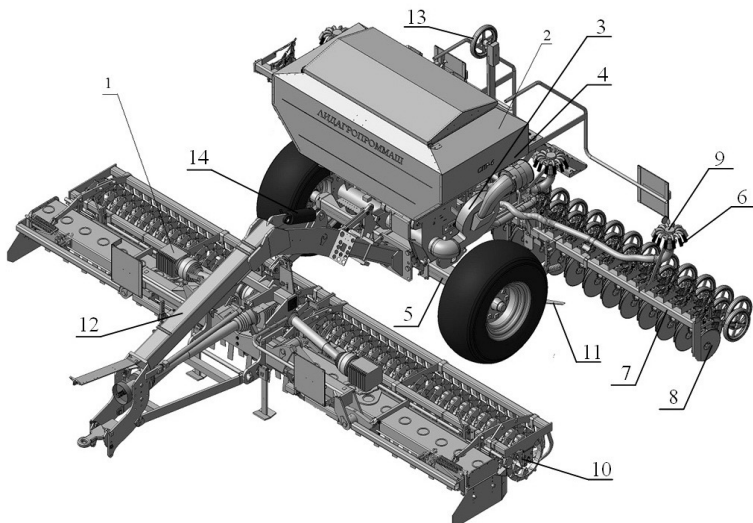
Общий вид почвообрабатывающе-посевного агрегата:
